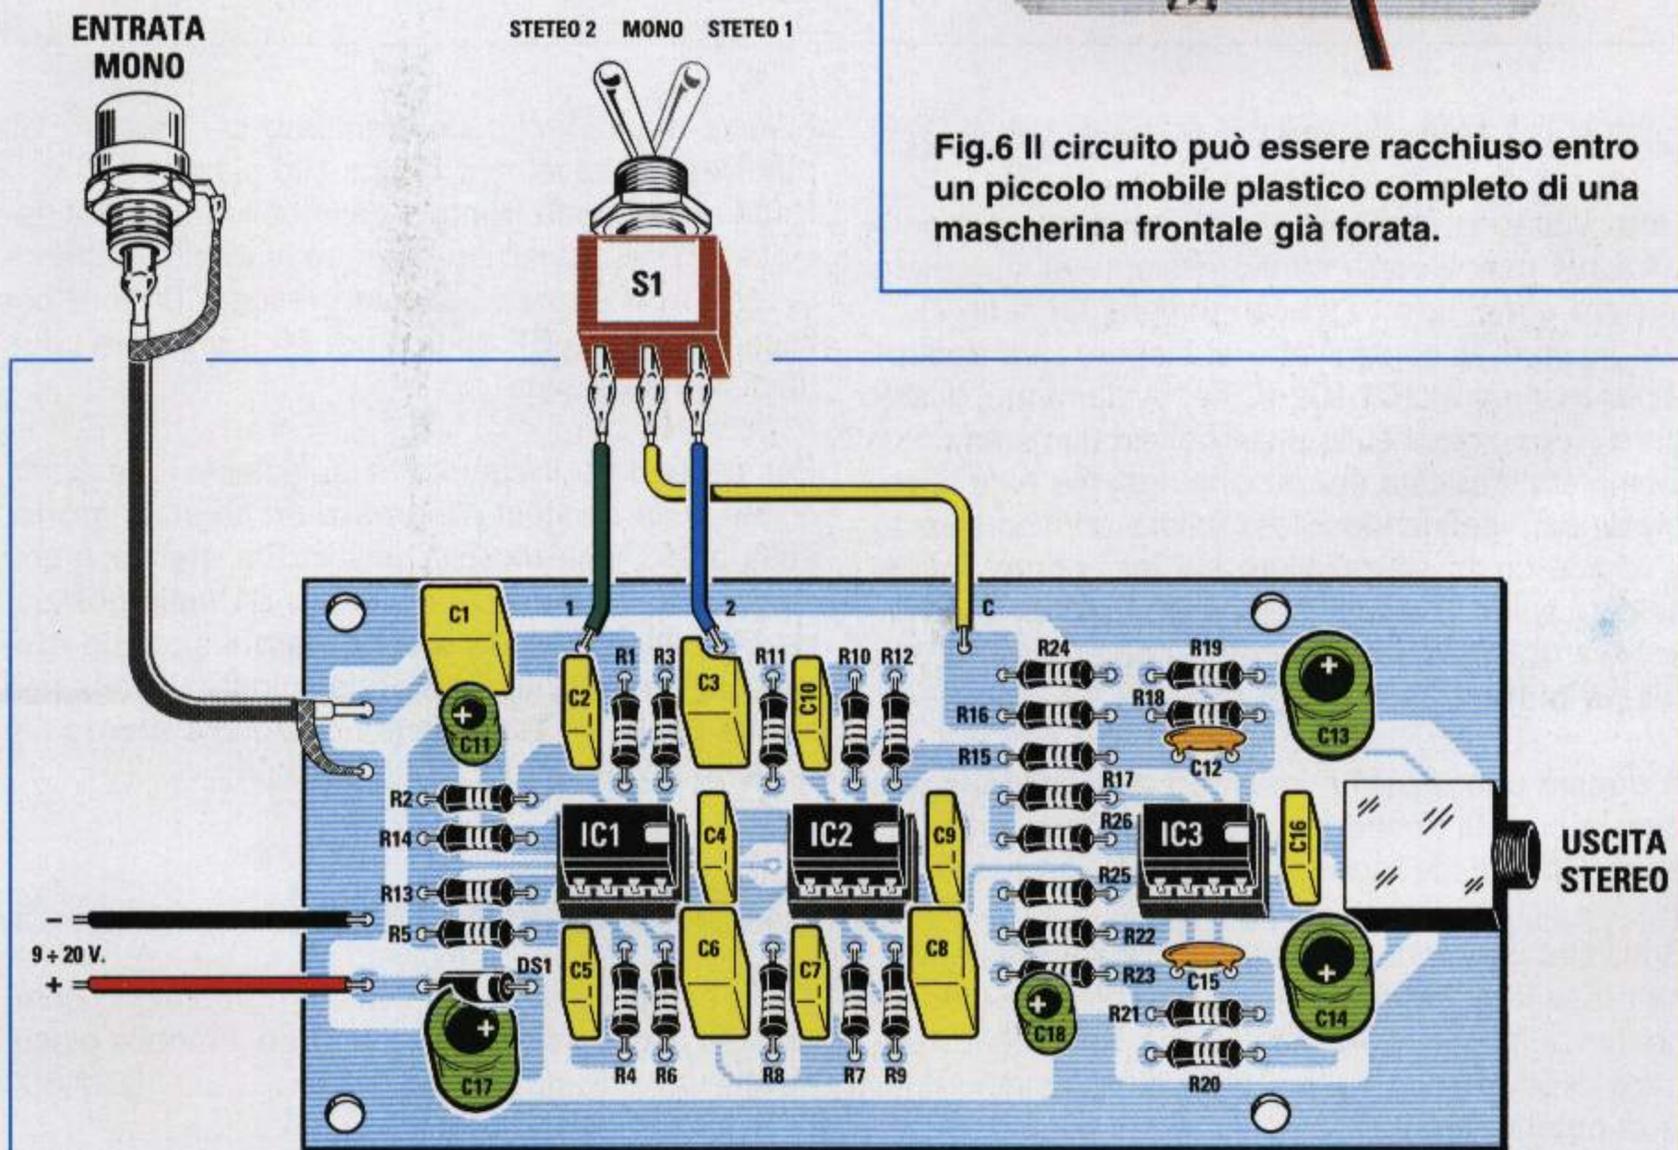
Schema pratico di montaggio del kit LX.1391. Il jack maschio della cuffia Stereo va inserito nella presa jack femmina visibile sulla destra. Per portare il segnale Stereo sull'ingresso di uno stadio finale di potenza si deve utilizzare del cavetto schermato.
